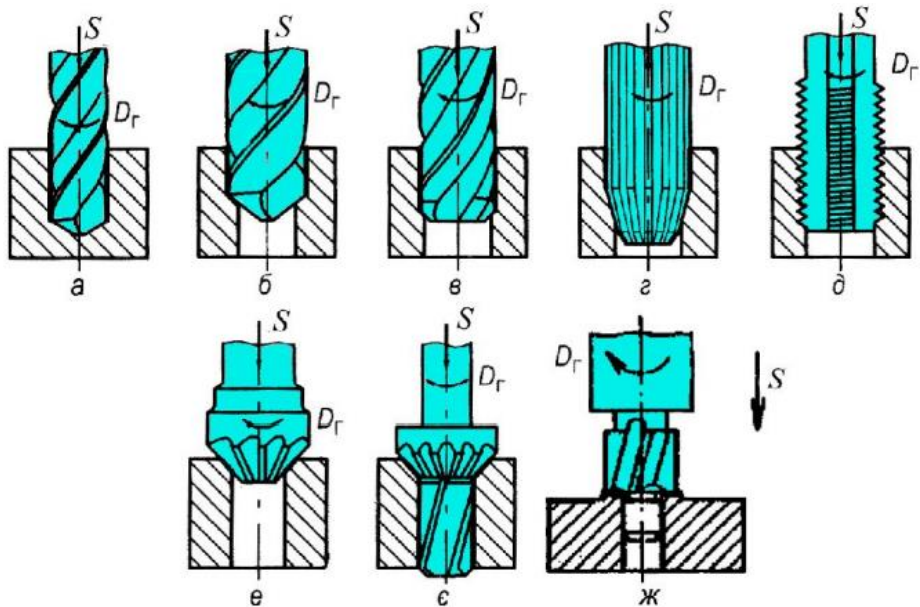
Види робіт, які можна виконувати на свердлильних верстатах: а – свердління; б – розсвердлювання; в – зенкерування; г – розверстування; д – нарізання внутрішньої різі мітчиком; е – зенкування конічної поверхні в отворі; є – обробка циліндричної та конічної поверхні в отворі комбінованим інструментом зенкер-зенківка; ж – цекування; ДГ – головний рух різання; S – рух подачі
